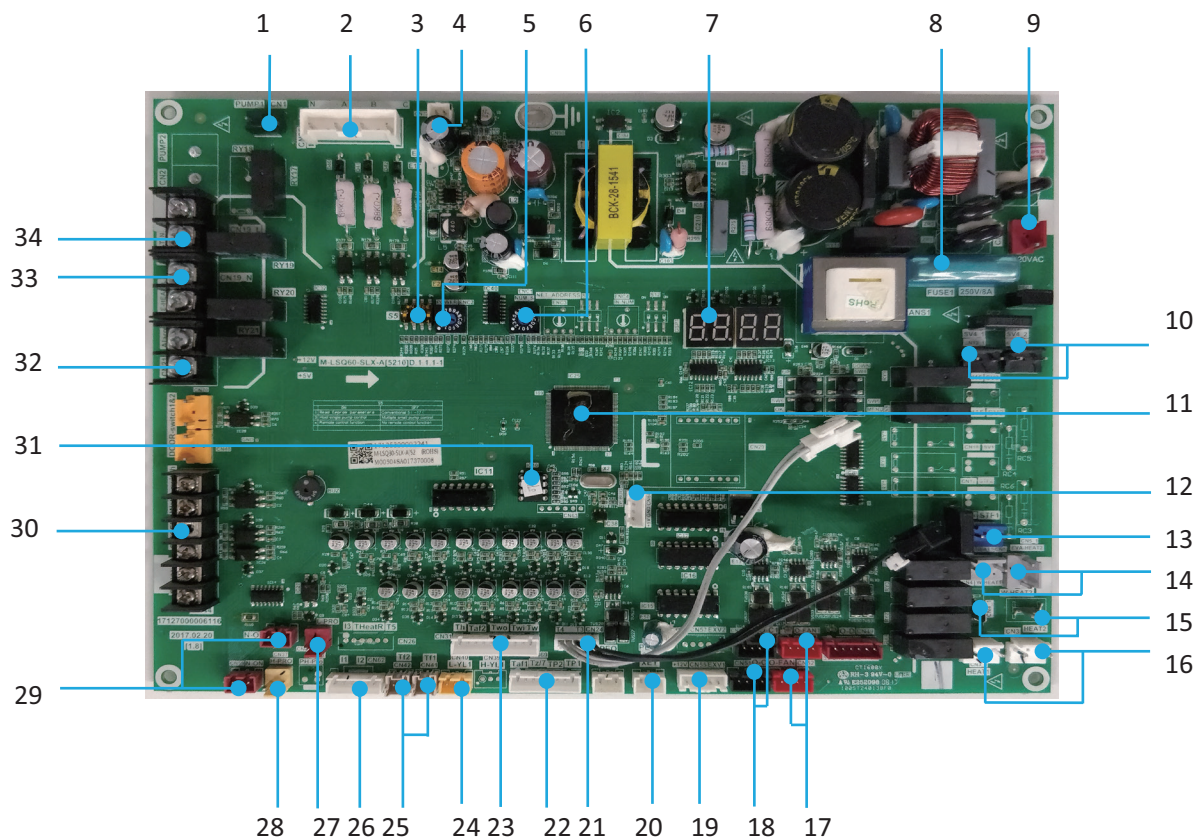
Blocul PCB principal KEM-90 DNS3
